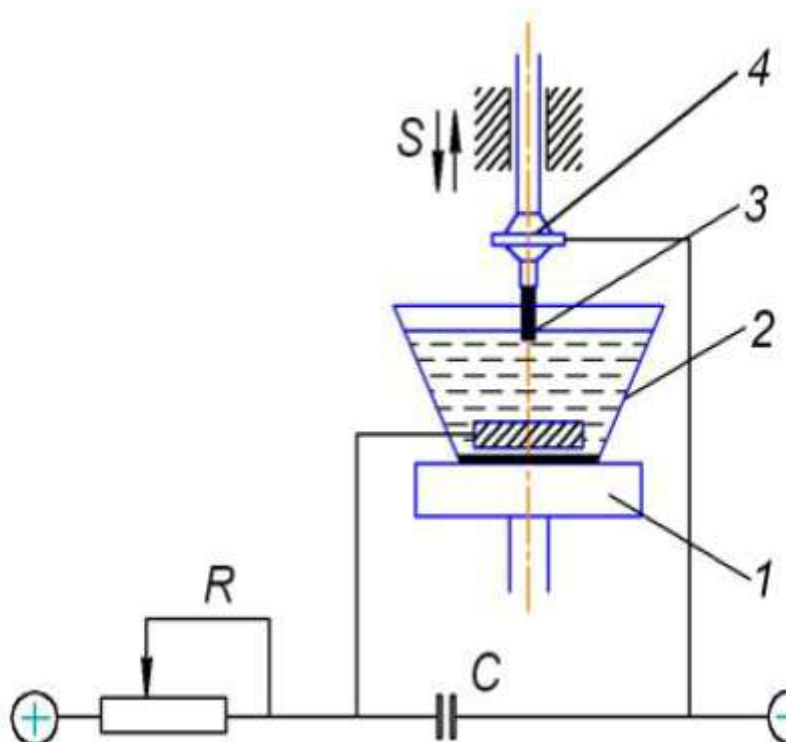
Принципова схема верстата для електроіскрової обробки ЛКЗ-57
